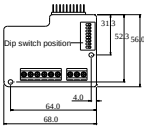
Размеры и установка платы инкрементальных энкодеров
